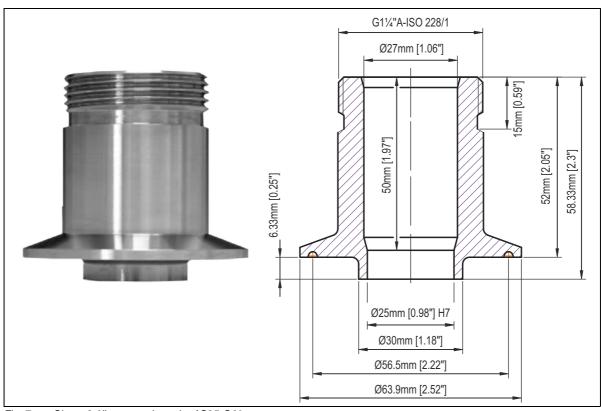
Clamp 2.0" puerto adaptador AS25-G60
